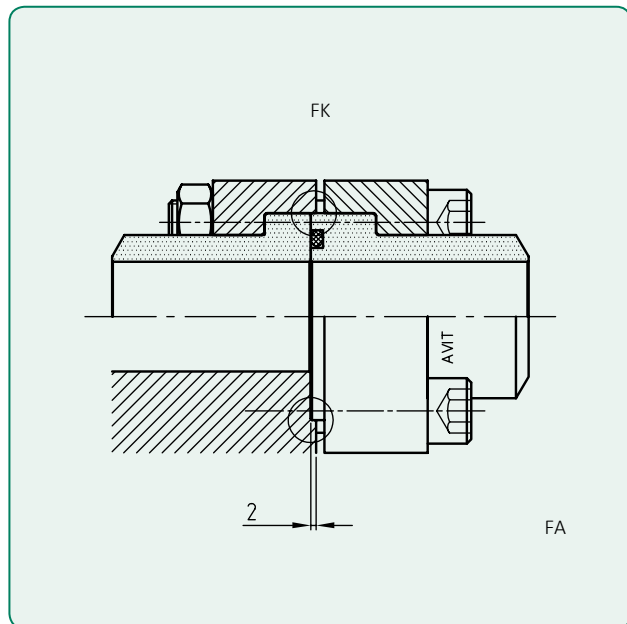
Schweißbund-Zentrierung | Welding piece centring
